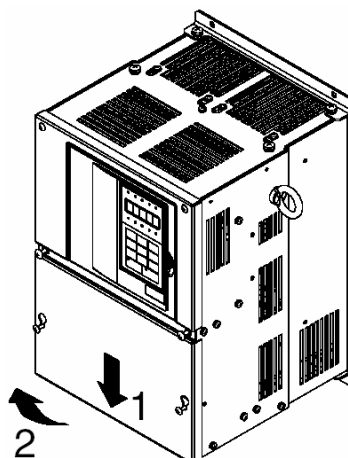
Montaje de la Cubierta de Terminales de Conexión.
